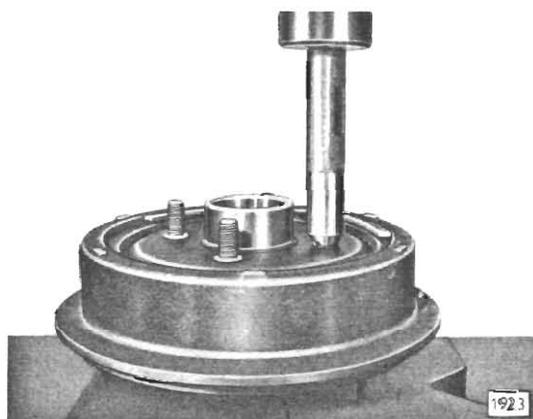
Radbolzen mit Vorderradbolzen-Stemmer S-1242 unter Presse verstemmen
